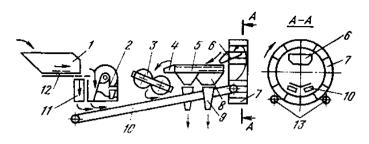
Схема одноагрегатной дробильно-сортировочной установки
